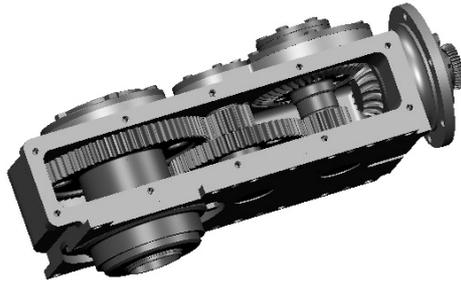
3D-сборка коническо-цилиндрического редуктора
